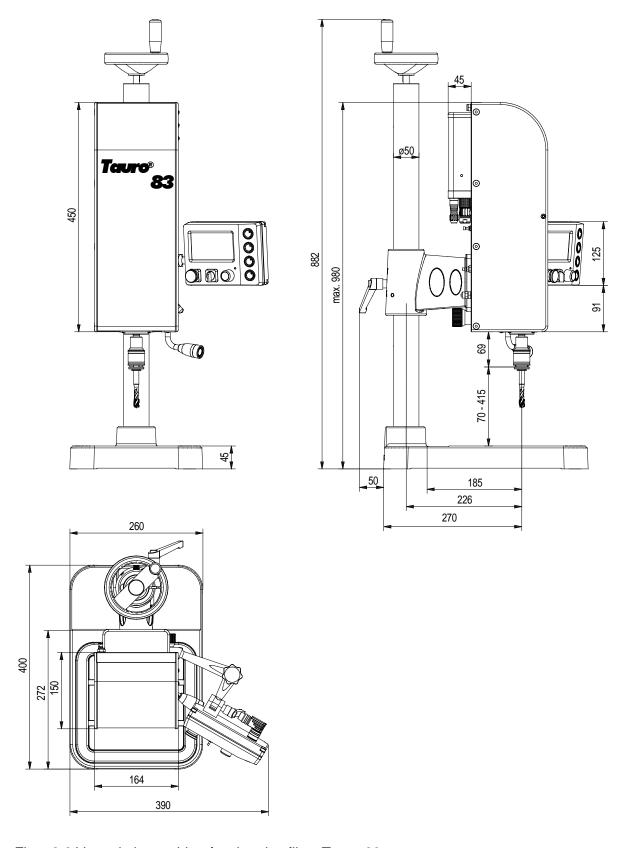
Vues de la machine à usiner les filets Tauro 83
